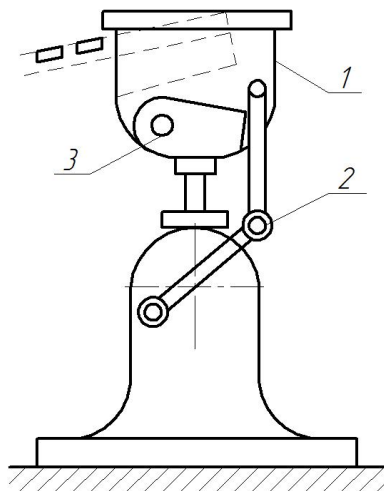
Схема секторного бункера: 1 – бункер; 2 – кривошипний механізм; 3 – скидач, сектор сам викидає заготовки
